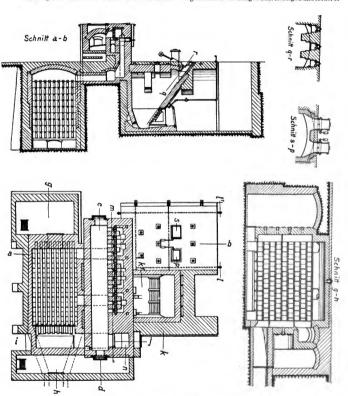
Rekuperator - Röhrenschweißofen.
